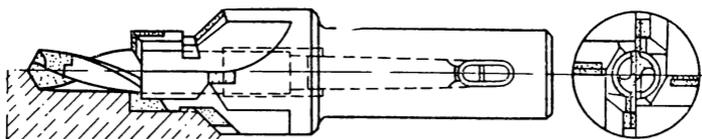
Комбинированный инструмент для обработки нескольких ступеней
